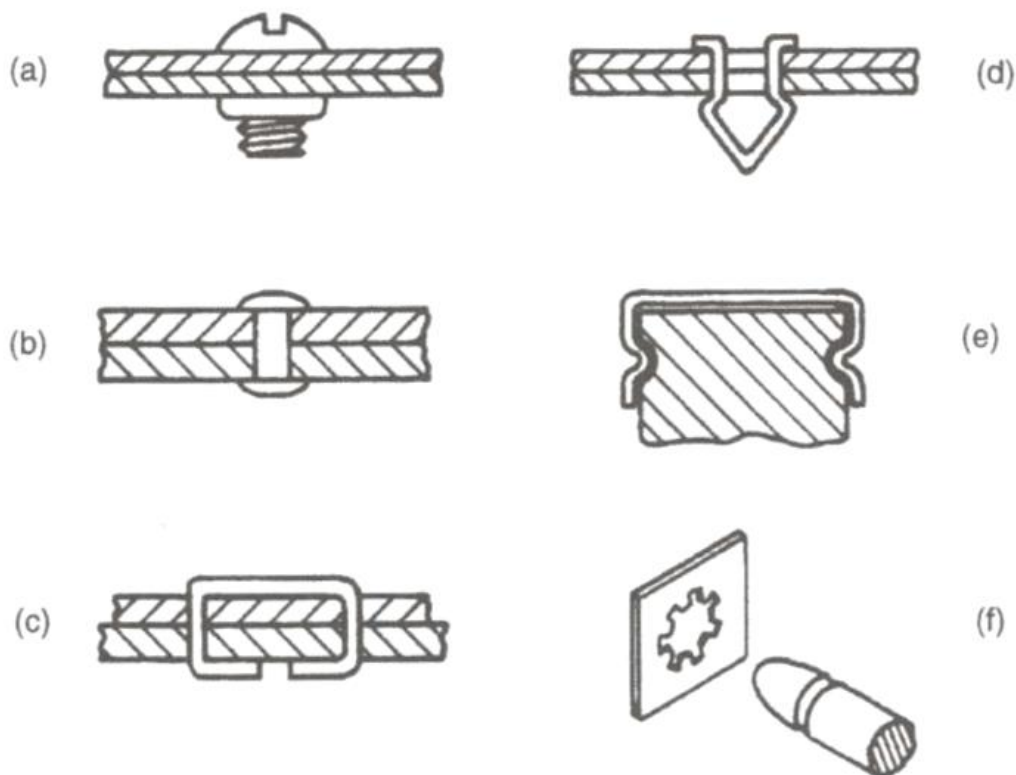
Pièces d'assemblage :(a) boulon ;(b) rivet ;(c) à (f) encliquetage.
